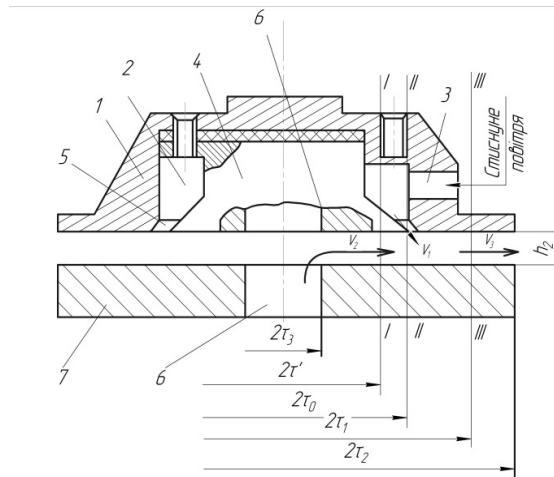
Розрахункова схема струминного захоплювача для кільцевих заготовок:
